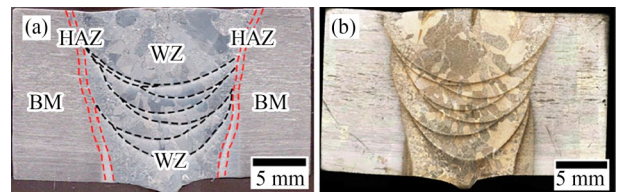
焊接接头横截面:(a)焊接区域;(b)截面宏观形貌^[21]
